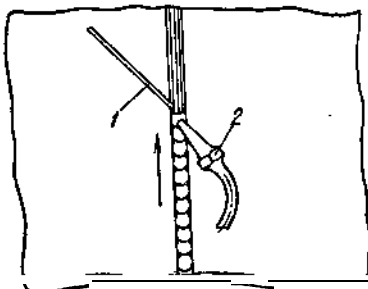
Положение горелки и присадочной проволоки при выполнении вертикального шва снизу
